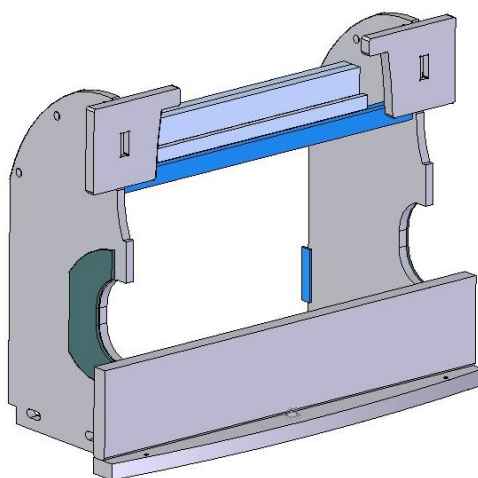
Representação da estrutura da quinadora idealizada após fabrico de soldadura e pré maquinagem.
